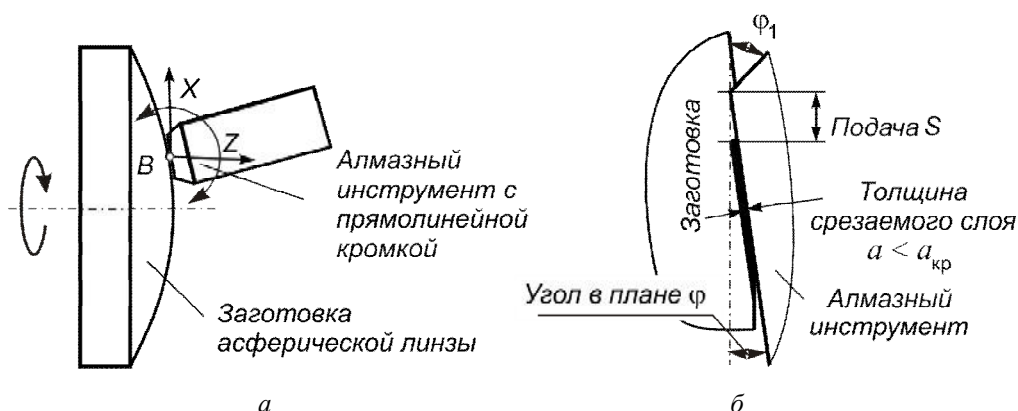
Схематическая модель обработки асферической поверхности инструментом с прямолинейной режущей кромкой [43]: *а* – кинематическая схема обработки; *б* – схема срезания слоя
